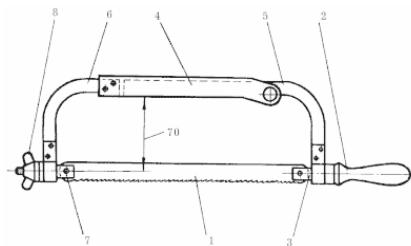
Ножовка ручная: 1 – полотно ножовки; 2 – рукоятка; 3 – стержень; 4 – обойма; 5,6 – правая и левая полурамки; 7 – натяжной винт; 8 – барашек.
